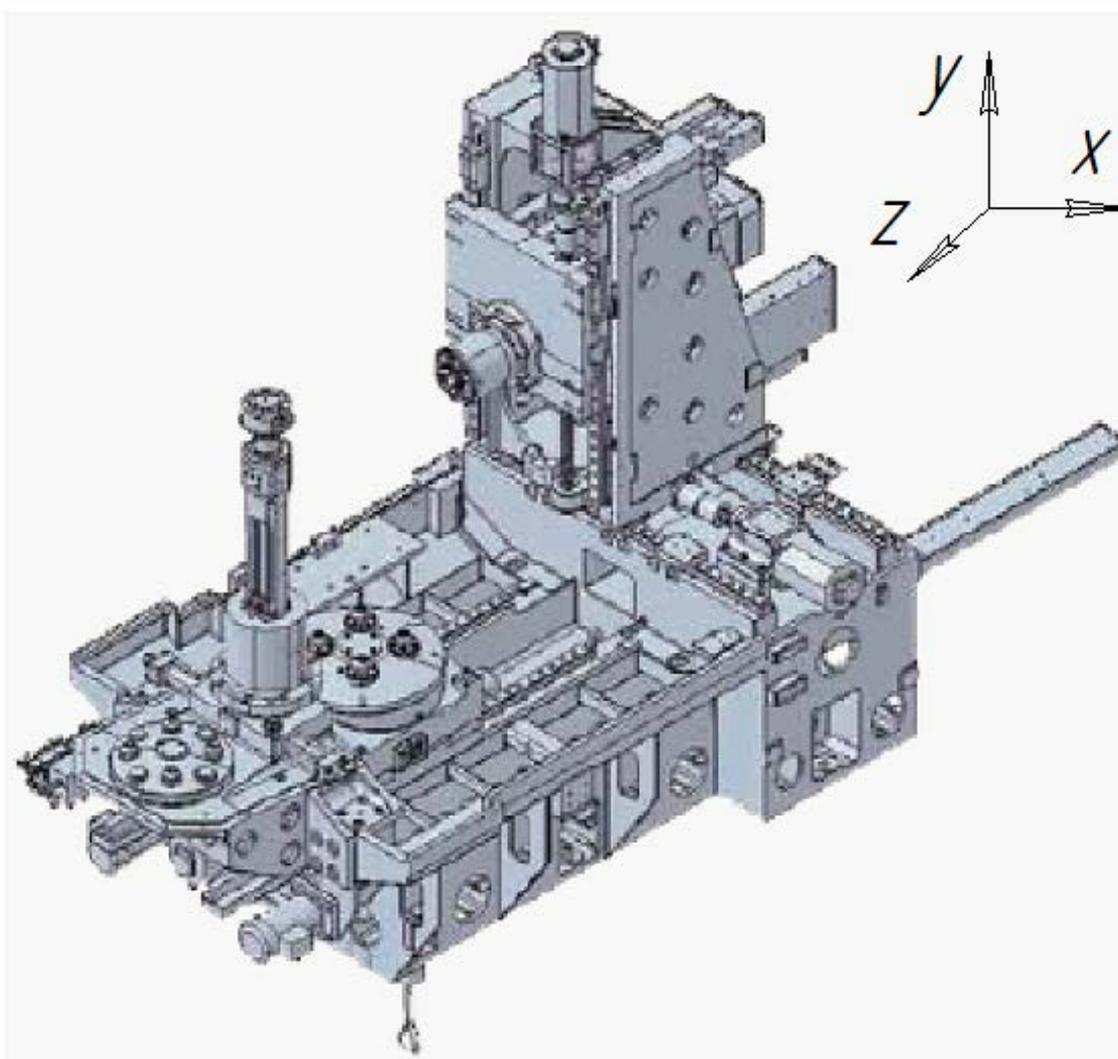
Компоновка и основные направления движения обрабатывающего центра DOOSAN HC500II
